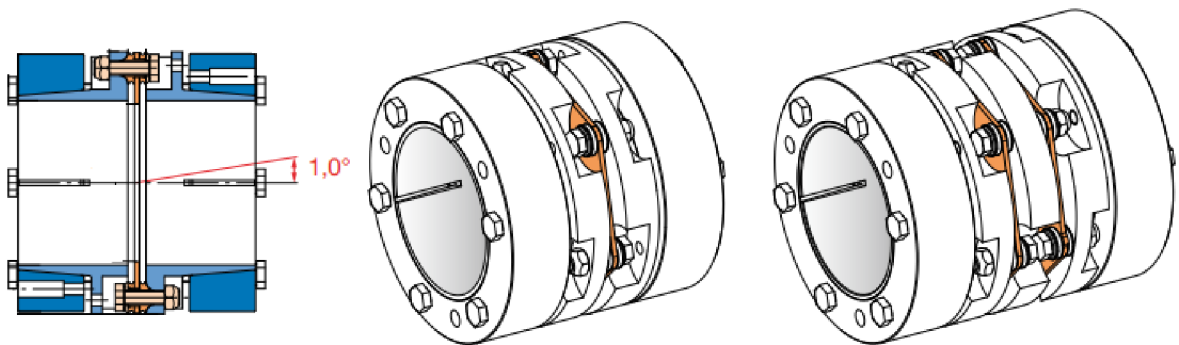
Uložení motoru a další komponenty pohonného ústrojí
